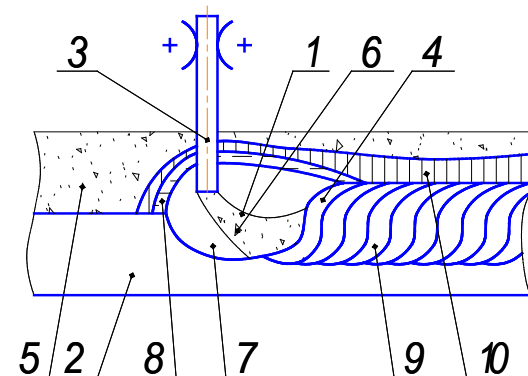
Автоматическая сварка под слоем флюса
